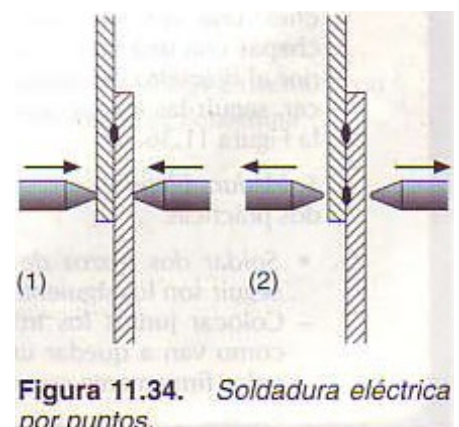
Soldadura eléctrica por puntos.
